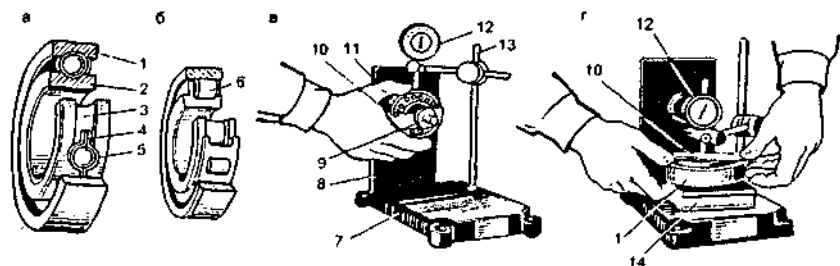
Устройство шарикового (а) и роликового (б) подшипников качения и приспособления для проверки радиальных (в) и аксиальных (г) зазоров
